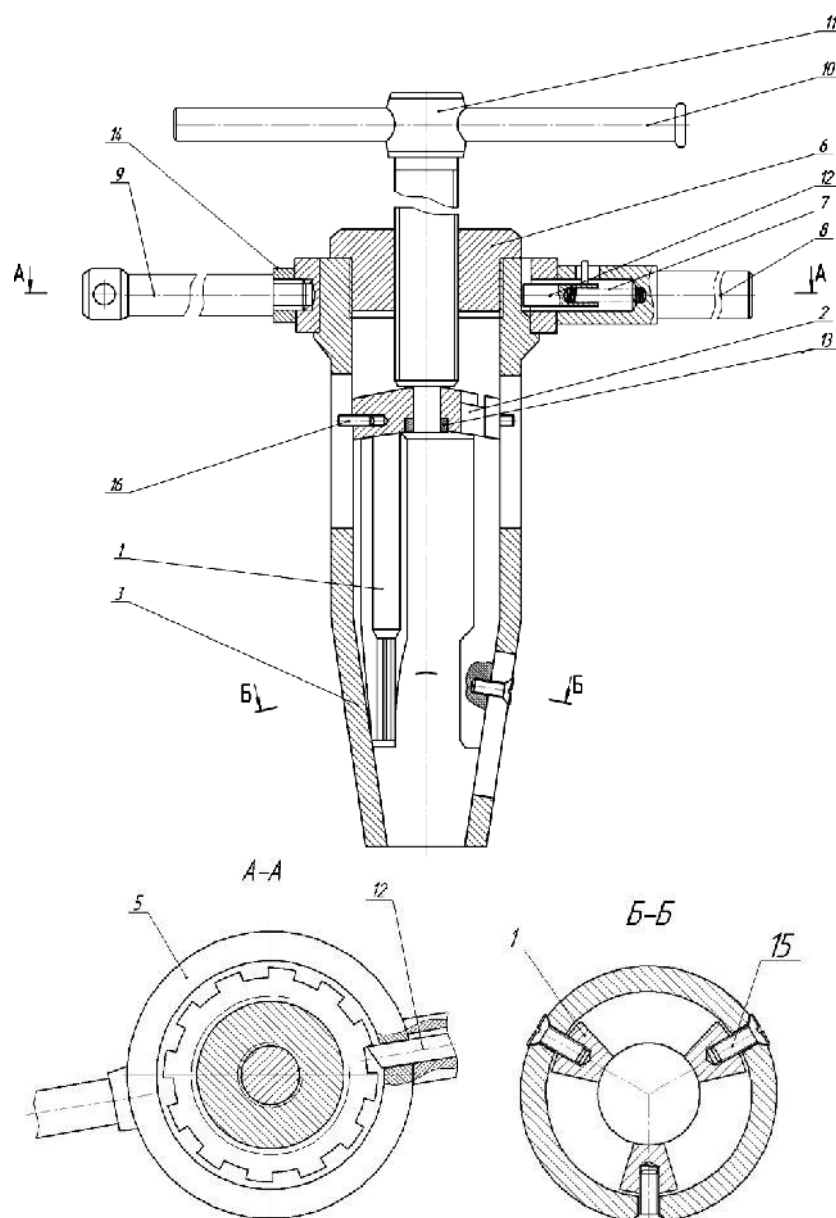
Приспособление для снятия и установки шпилек
